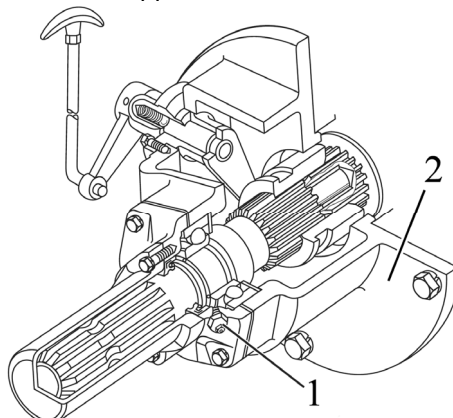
Смазка нижнего подшипника вала механизма поворота
